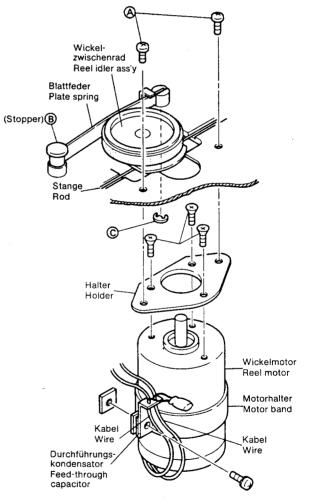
Wickelmotor und Wickelzwischenrad Fig. 3-6 Reel motor and reel idler replacement
